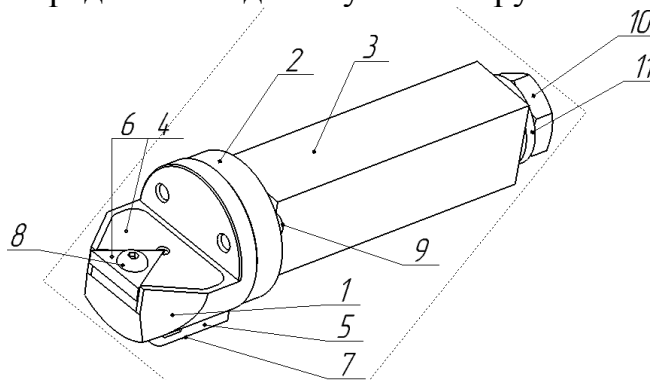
3D модель резца для безвершинного резания: 1 – основание резца, 2 – ось, 3 – державка, 4 – крышка, 5 – заглушка, 6 – СМП, 7 – болты крепления заглушки, 8 – винт крепления СМП, 9 – болты крепления основания и оси резца, 10 – болт М18, 11 – шайба, 12 – опорная пластина
